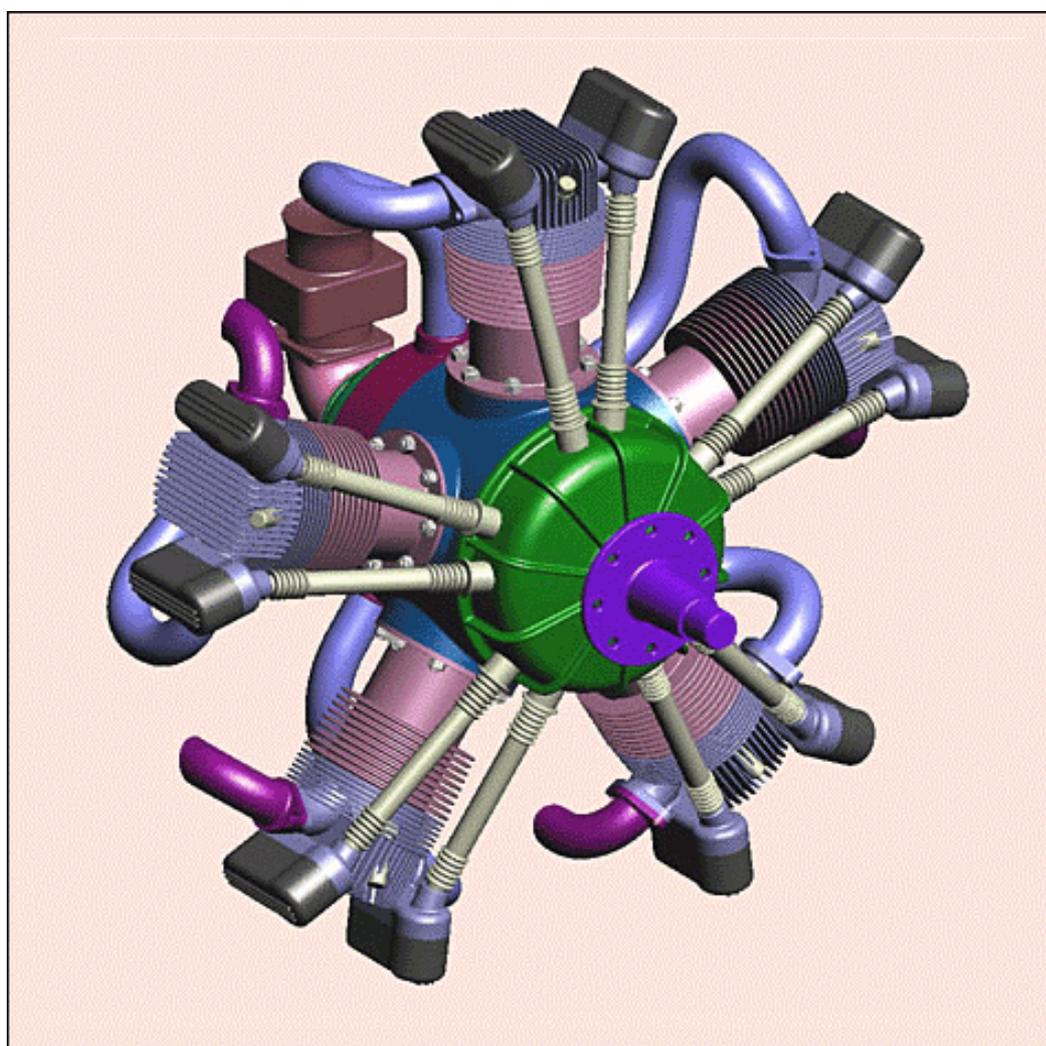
Пятицилиндровый двигатель (Pro/ENGINEER)
